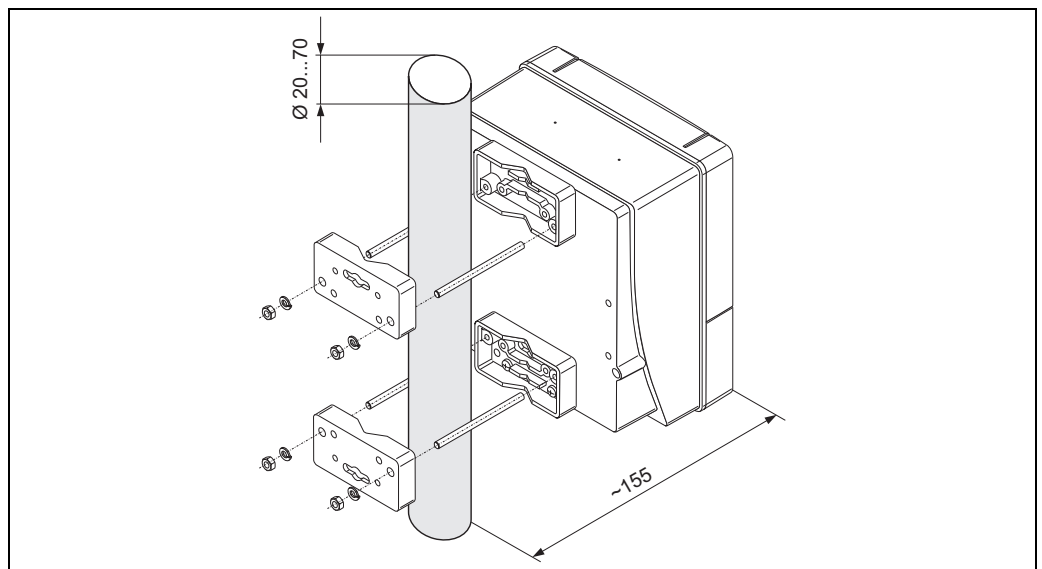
Rohrmontage (Wandaufbaugehäuse)
